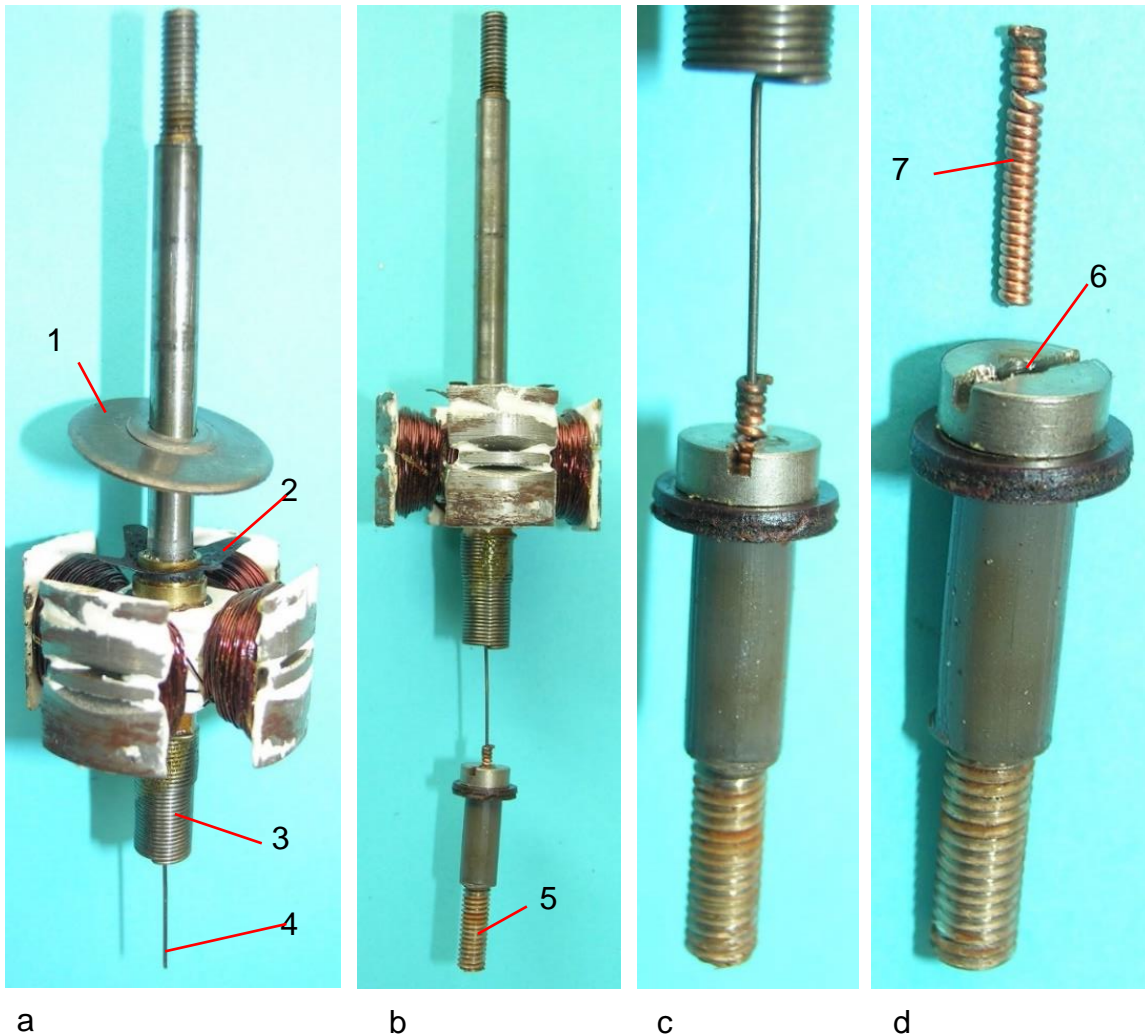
Spannung führender Kontakt: 1-Anlaufscheibe, 2-Axialspielausgleichsfeder, 3-Feder zur Befestigung des Schleifdrahtes, 4-Schleifdraht, 5-Kabelanschlussbolzen, 6-Bürstenhalter, 7-Bürste
